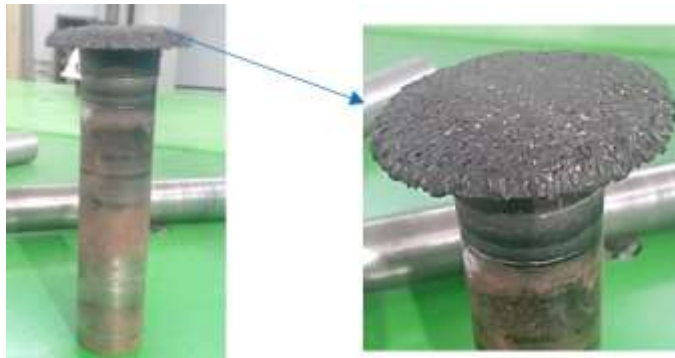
Дефект у вигляді «корони» з розплавленого металу на торцевій поверхні заготовки після ротаційного плазмового розпилення
